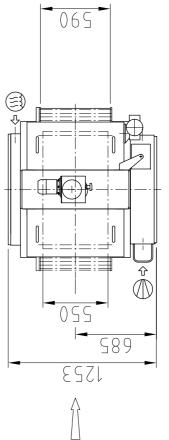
, Dimensiones LH (Versión mano izquierda)
